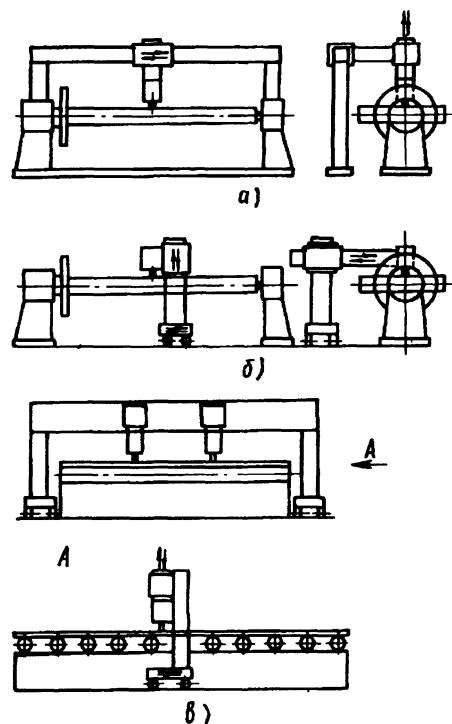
Типовые схемы компоновки установок для сварки прямолинейных швов изделий типа балок и рам
